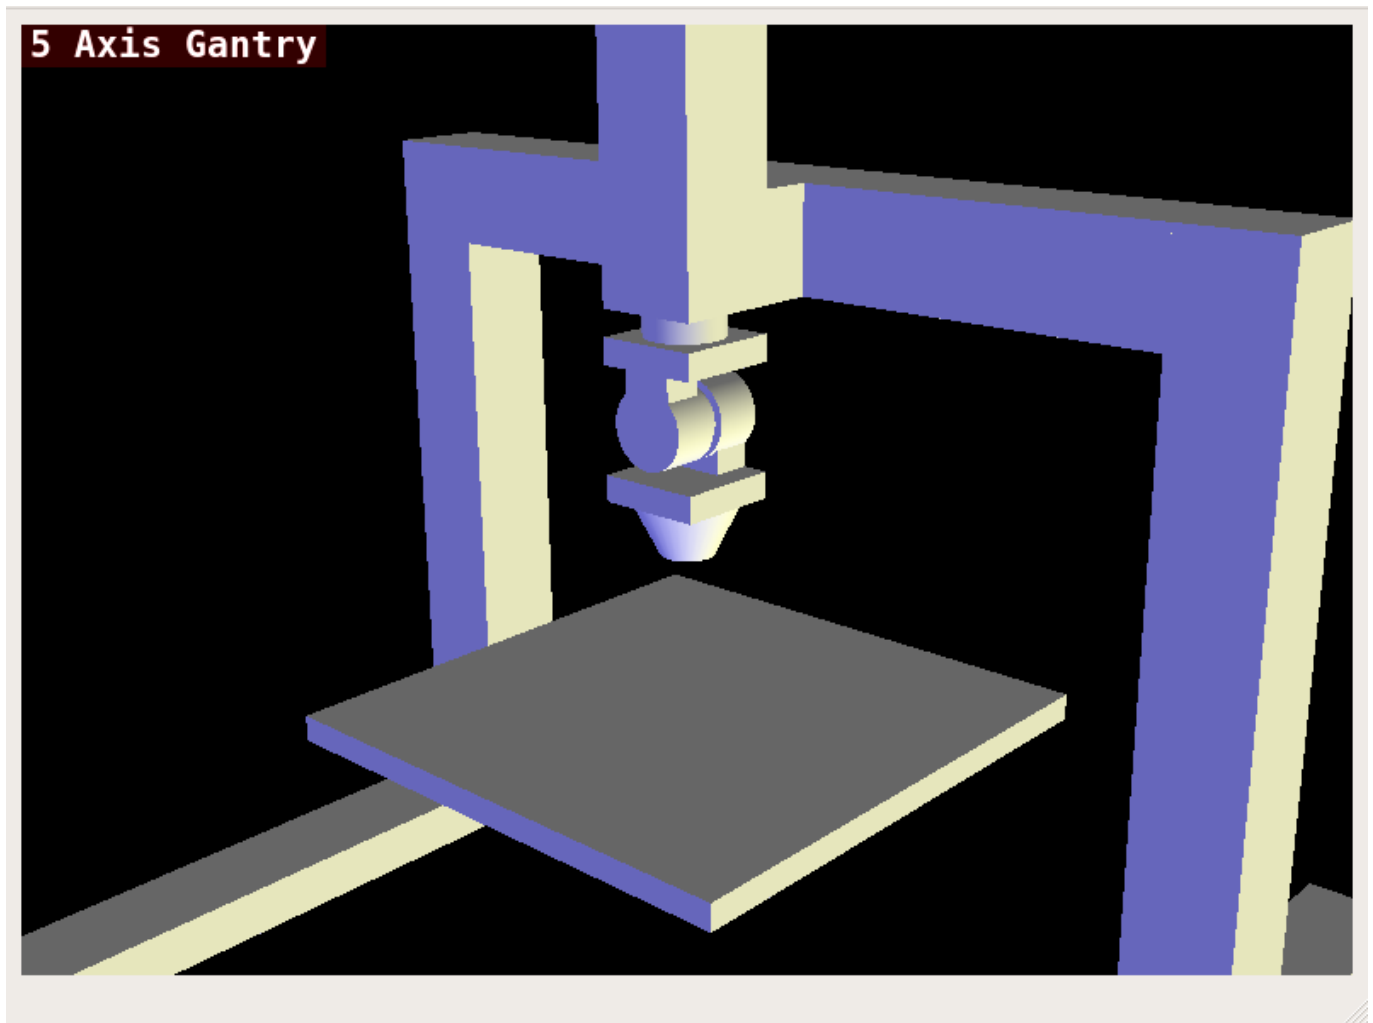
QtVCP vismach\_mill\_5axis\_gantry - 5-Axis Gantry Mill 3D View Panel
